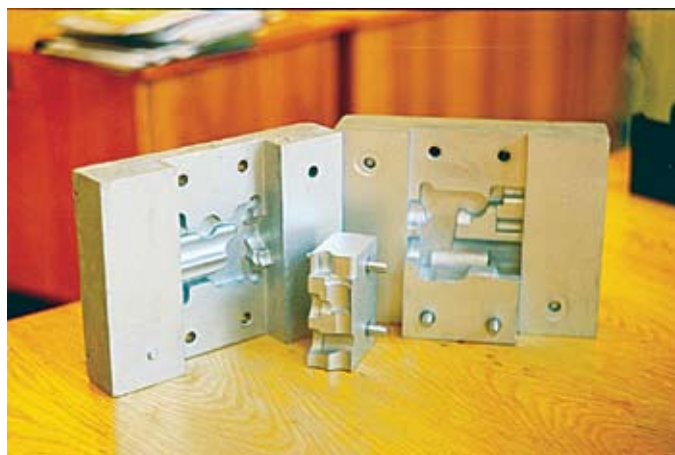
Литейная оснастка из композитного материала для изготовления корпуса методом литья по выплавляемым моделям
